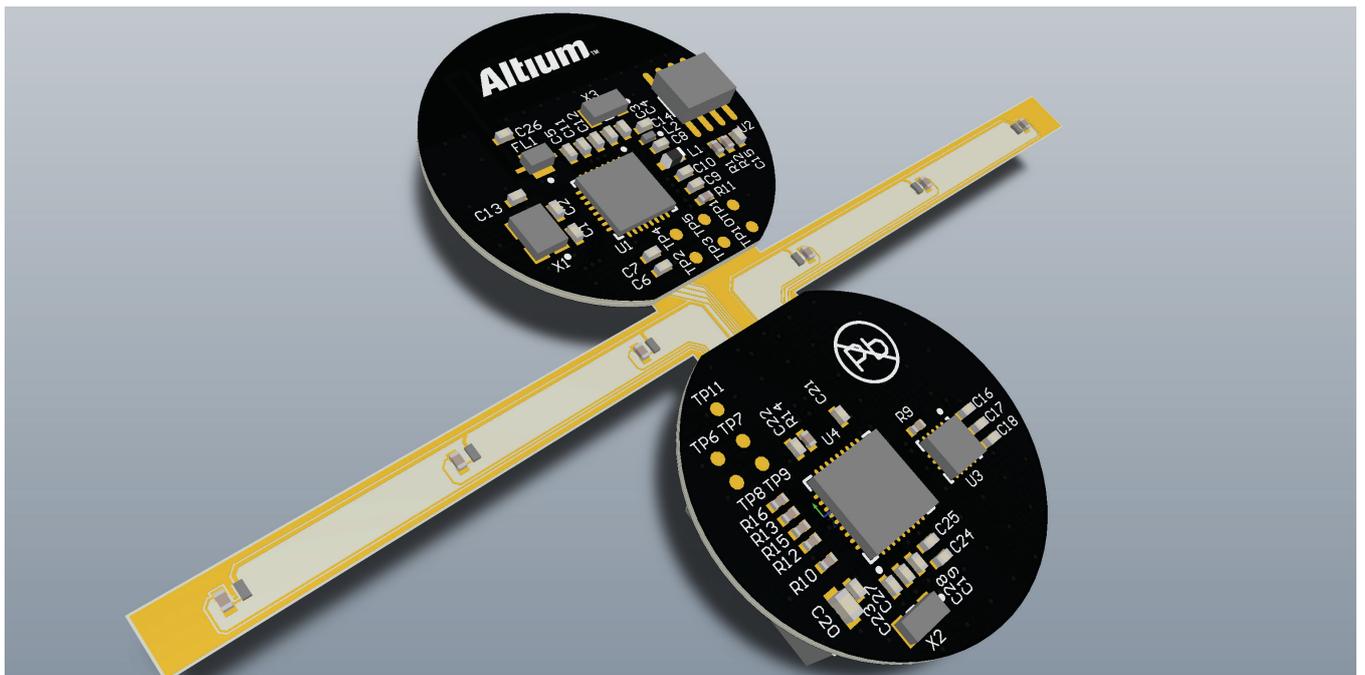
El software de diseño de PCB que proporciona un modelado 3D permite a los diseñadores ver exactamente cómo se ajusta el ensamblaje del PCB.
